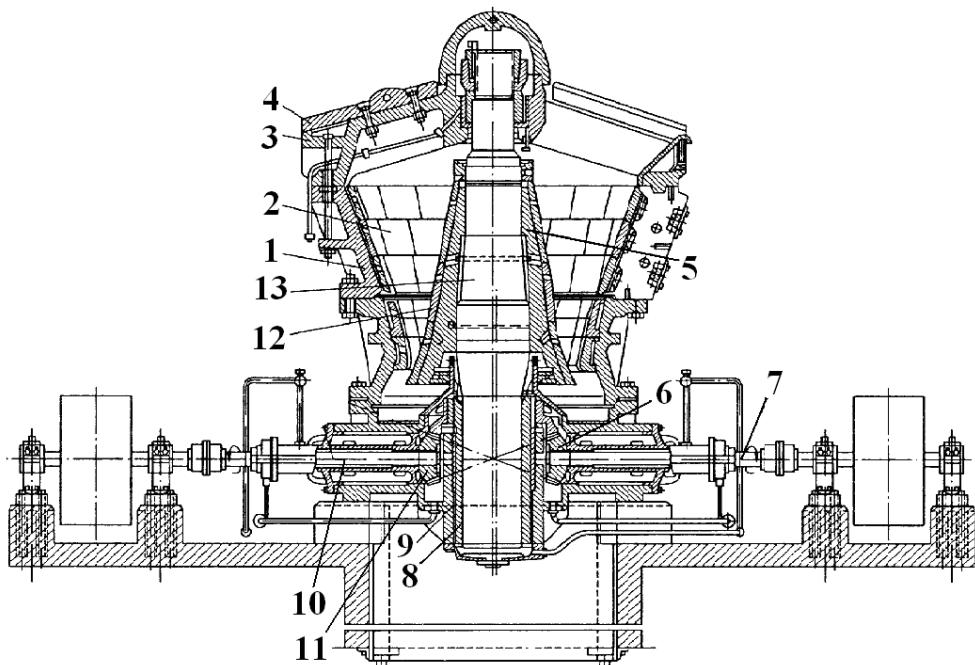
Конусная дробилка с подвесным валом для крупного дробления типа ККД
